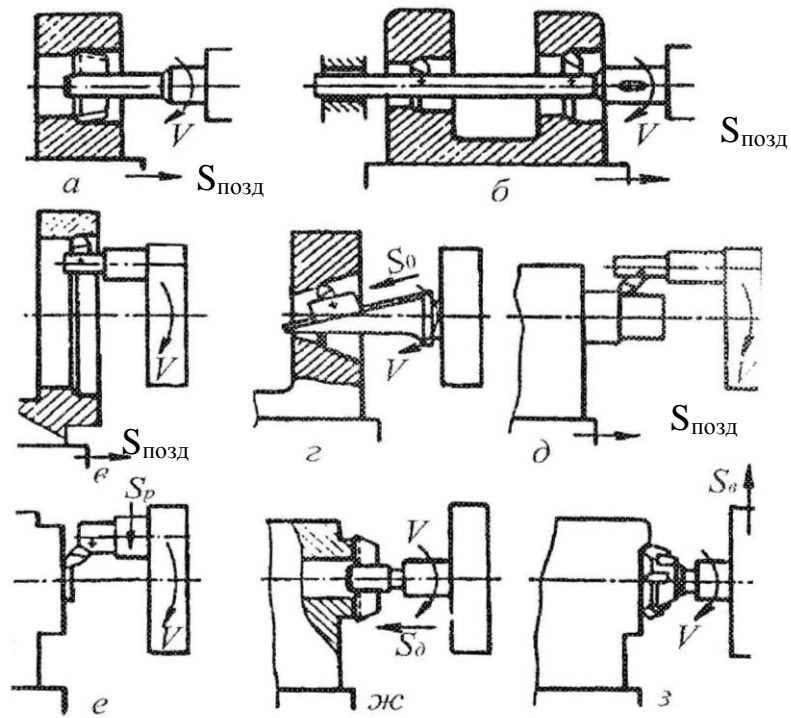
Схеми обробки поверхонь заготовок на горизонтально-розточувальних верстатах
